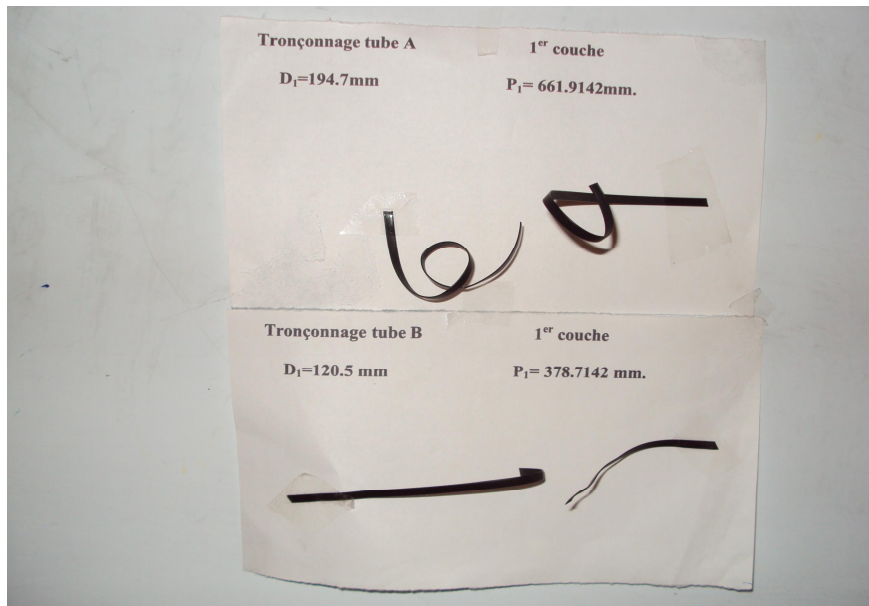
Représentation de deux éprouvettes. En haut tube A, en bas tube B.
